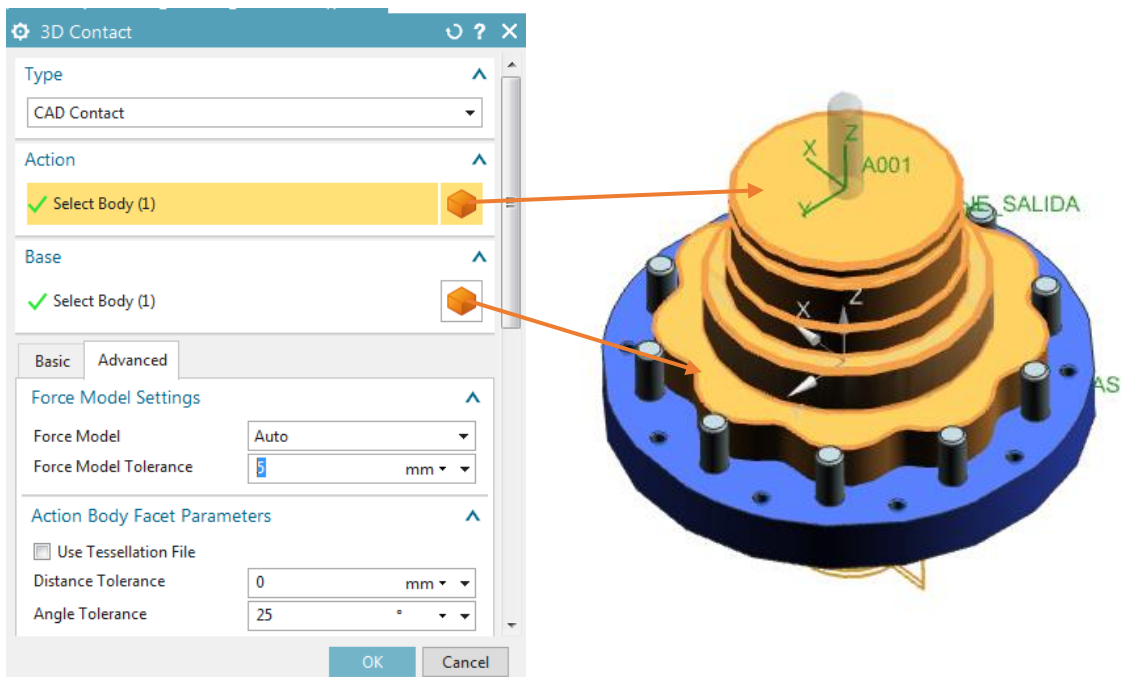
Contacto G002 entre eje de salida- Engranaje
